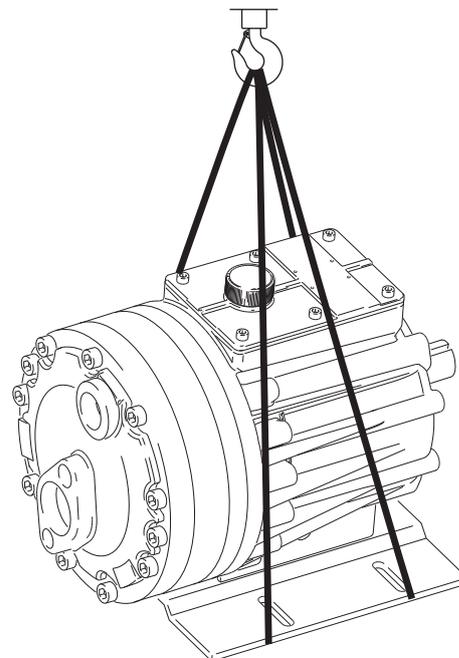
Hebezeug befestigen an Pumpe (Beispiel 2)
